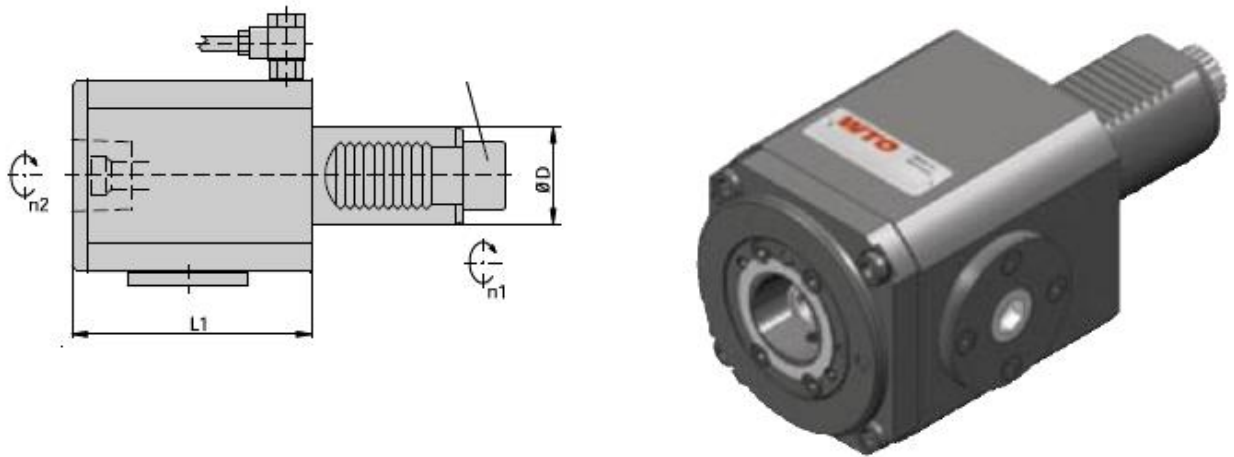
Прямий свердлильно – фрезерний блок.
